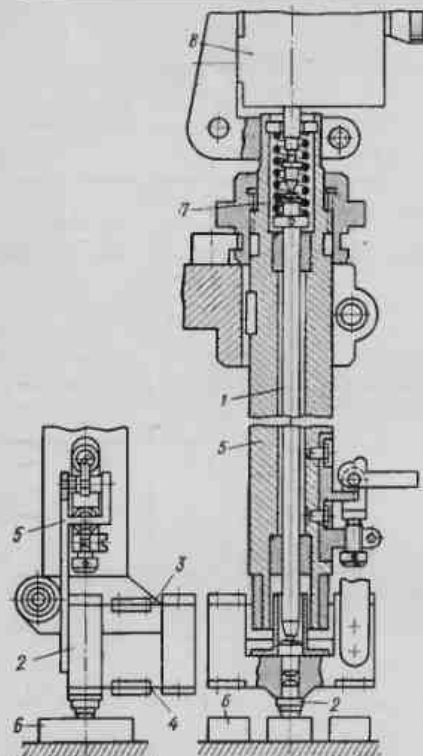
Устройство для контроля высот деталей, обрабатываемых на плоскошлифовальных станках
